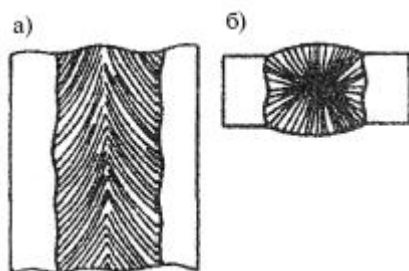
Направление столбчатых кристаллитов в швах, выполненных электрошлаковой сваркой: а – разрез вдоль шва; б – разрез поперек шва
